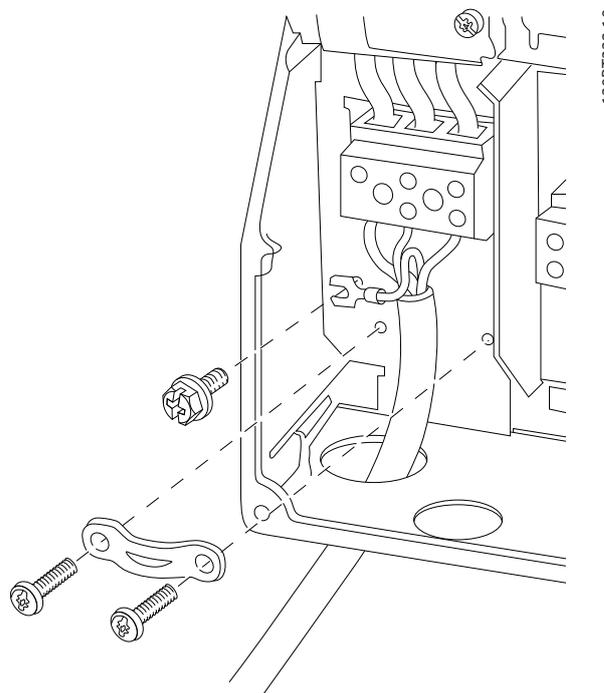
Raccordement au secteur des protections de tailles B1 et B2
